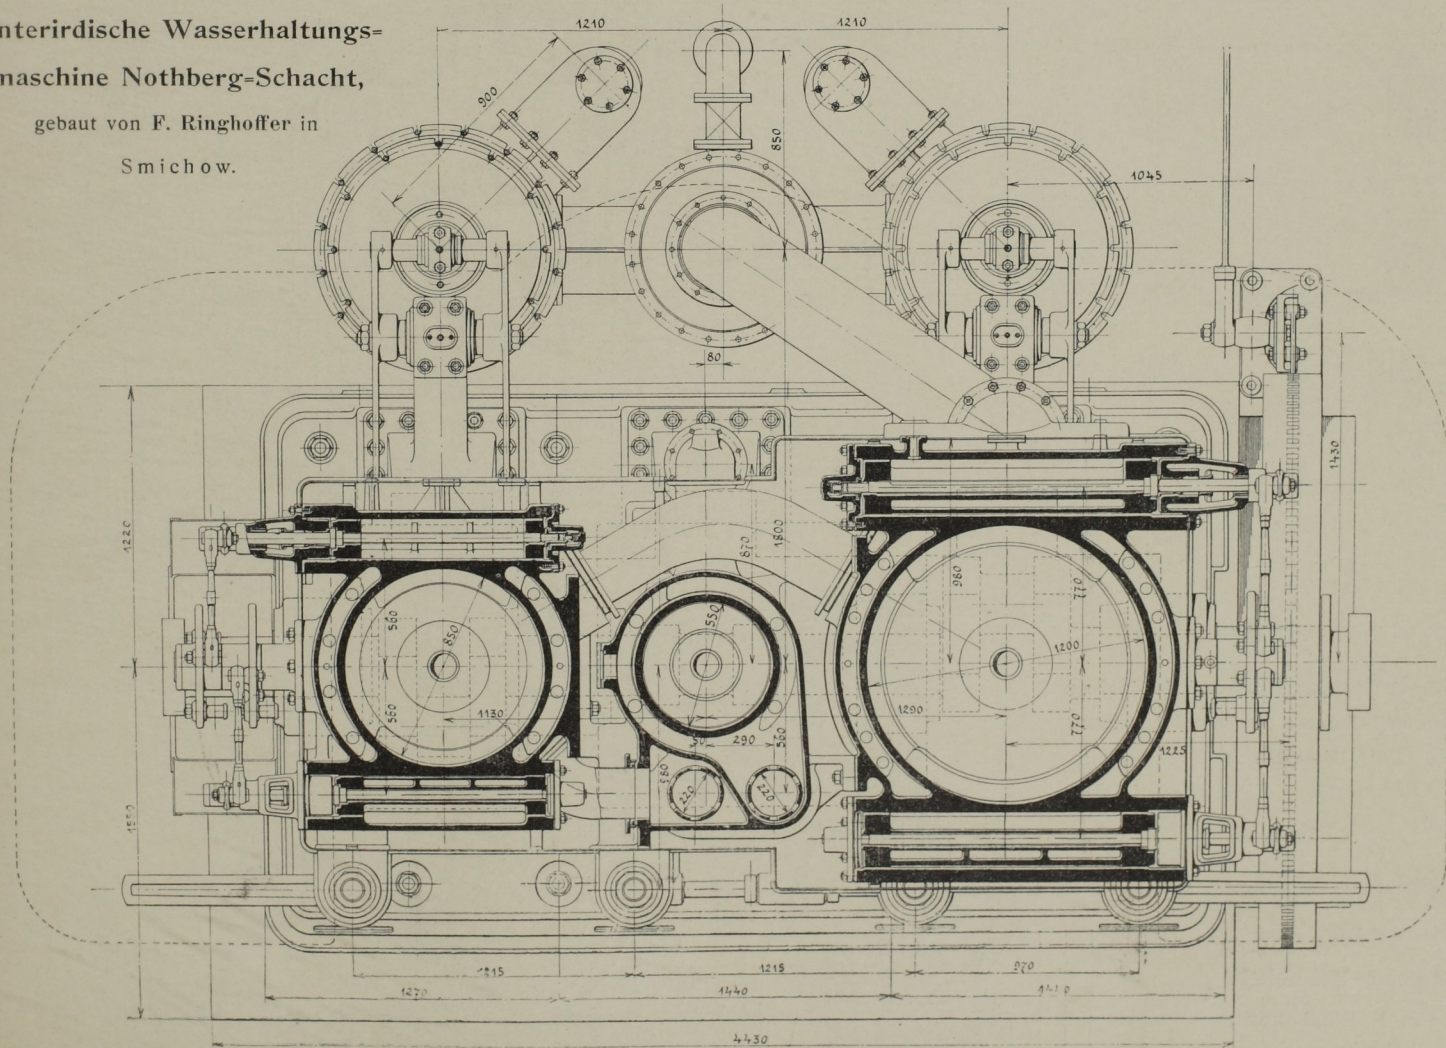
Grundriss der Dampfmaschine. Massst. 1:30.
